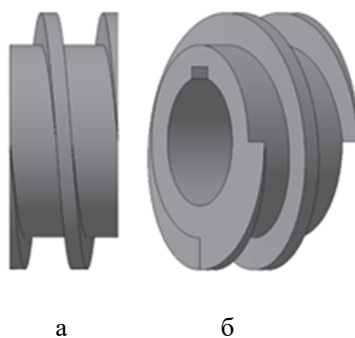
Стандартная шнековая втулка, выточенная на винторезном оборудовании из цельной заготовки: а – вид сбоку; б – вид под углом
